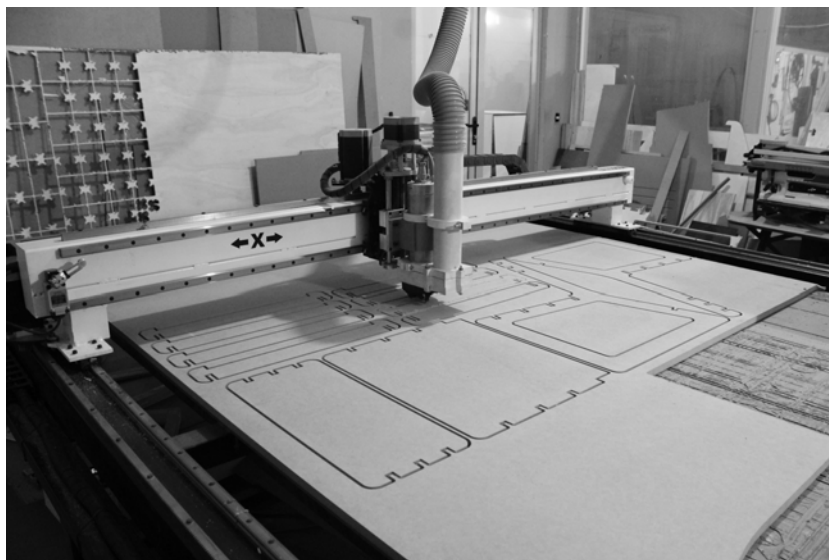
Máquina CNC cortando primeiro protótipo em escala real
